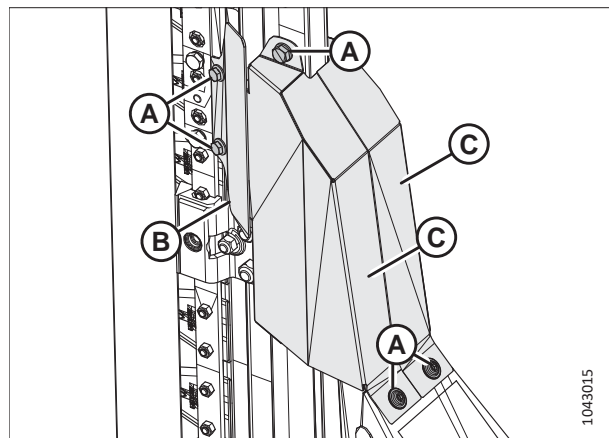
Entfernen der Befestigungselemente um das Messer
